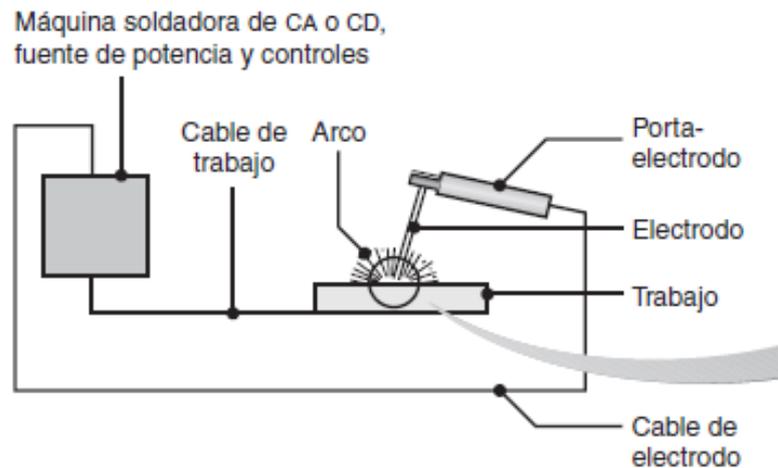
Esquema de soldadura con arco y metal protegido (Fuente: Manufactura, Ingeniería y Tecnología)
